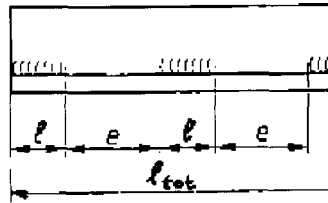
Berechnung der Scherkräfte auf unterbrochen geschweißte Schweißnähte
